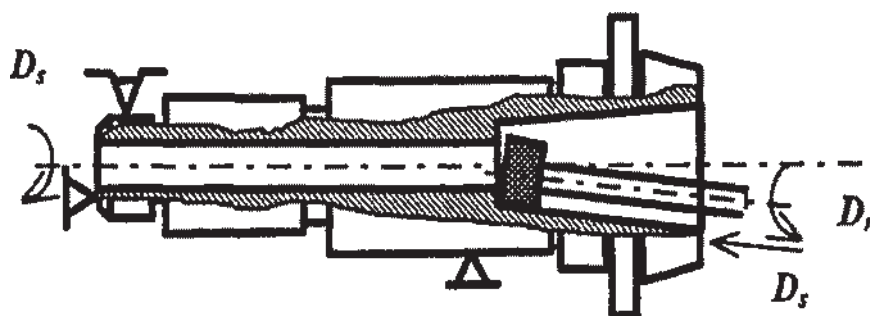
Схема обработки внутренних конических поверхностей на шлифовальном станке с поворотом шлифовальной бабки
